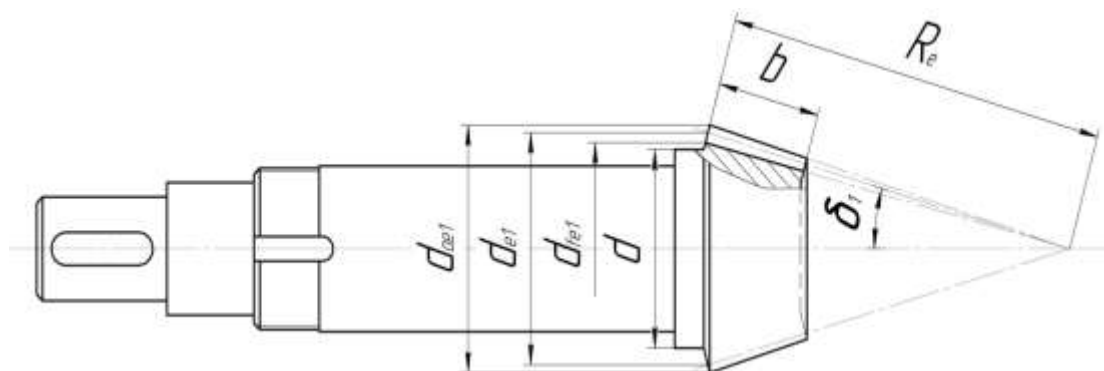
Конструкция вала-шестерни (конической)
